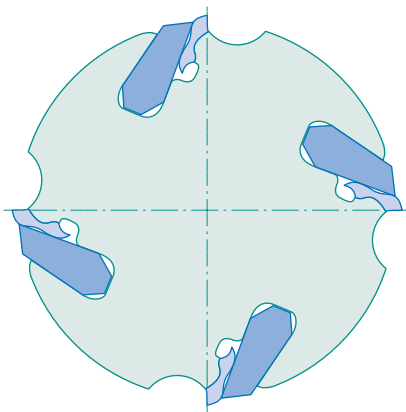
Vue en coupe du porte-outil dont les lames sont fixées sans vis - *Cross-sectional view of a tool holder, the blades of which are retained without screws
